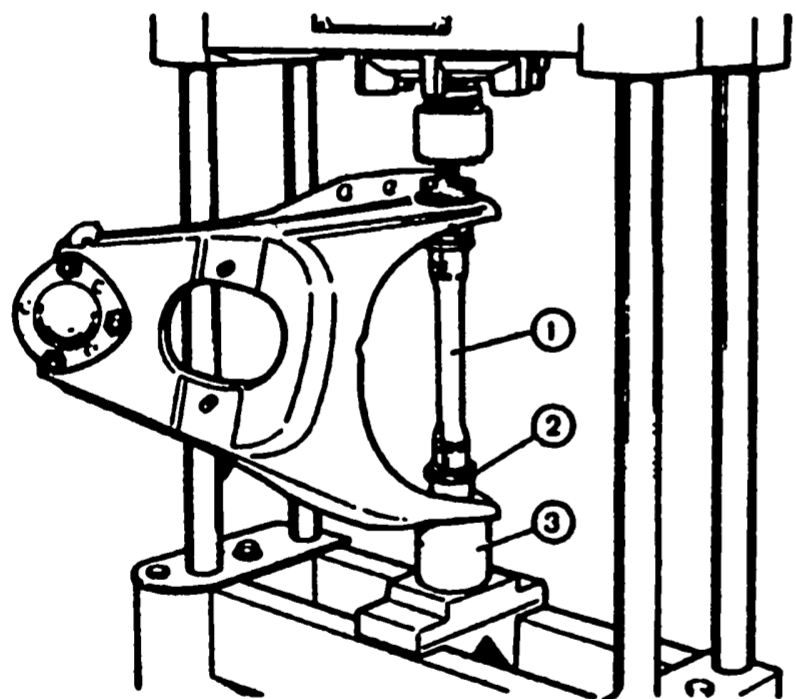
Выпрессовка шарниров нижнего рычага: 1 - ось рычага; 2 - шарнир рычага; 3 - оправка
